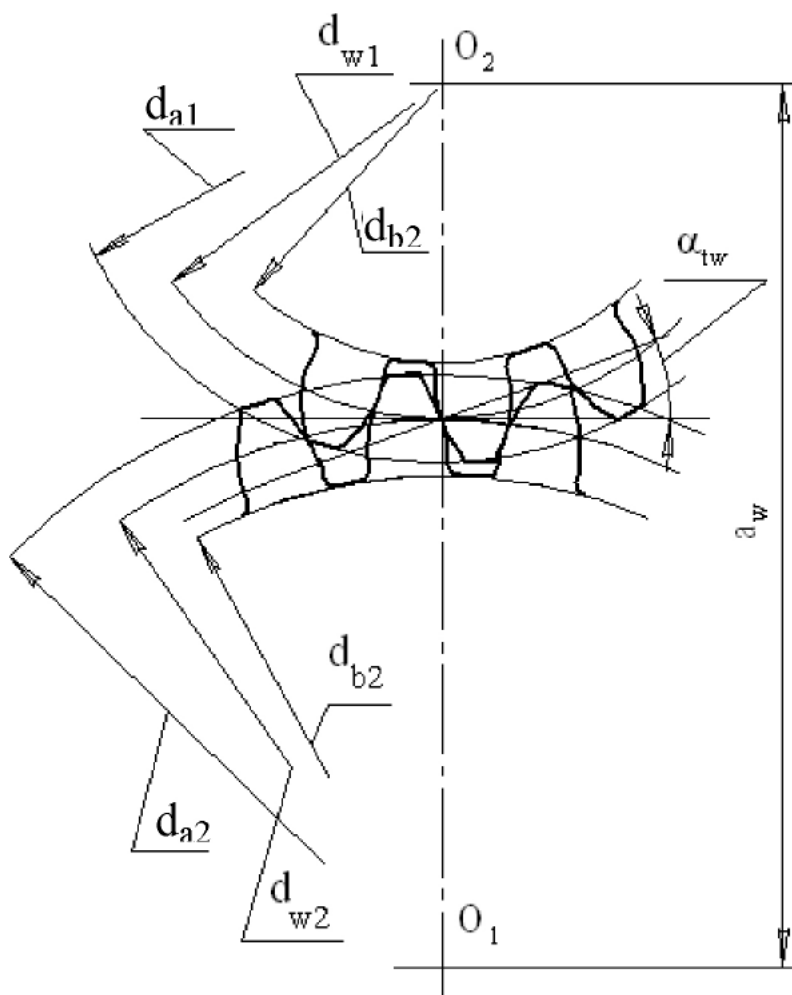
Основные размеры цилиндрической зубчатой передачи внешнего зацепления
